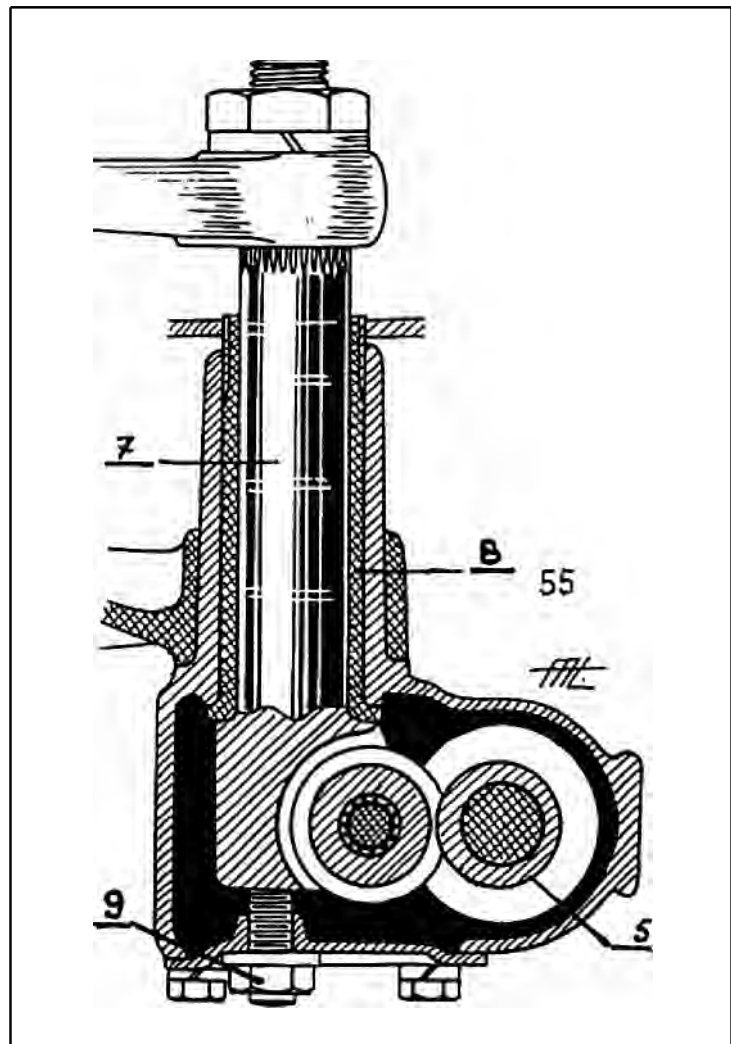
Coupe d'une direction à galet (Vue en plan)
